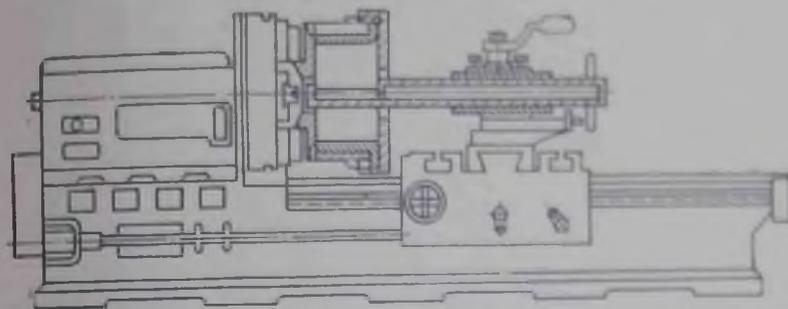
Нанесение покрытия центробежным способом на токарном станке
